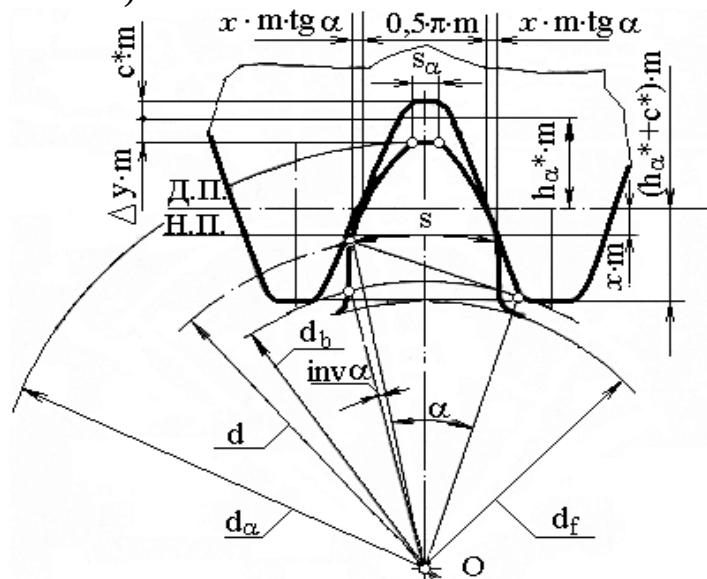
Зацепление зубчатого колеса с инструментальной рейкой:
